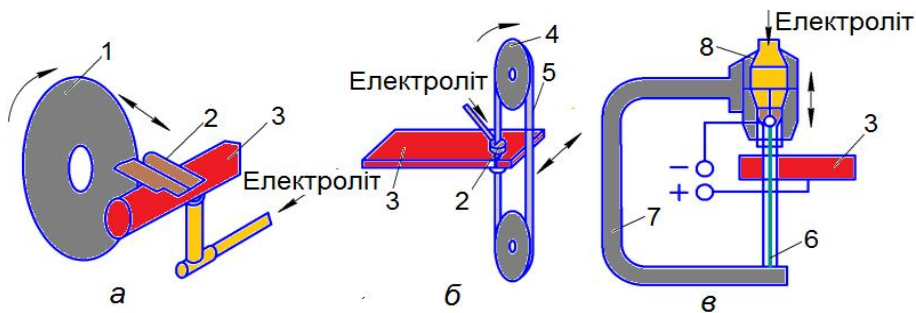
Схеми установки для розмірної електрохіміко-гідравлічної обробки шляхом різання:
